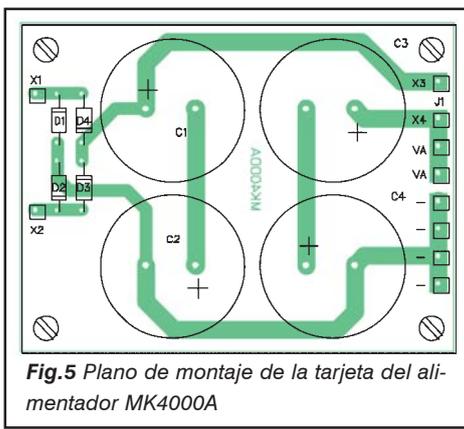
Plano de montaje de la tarjeta del alimentador MK4000A
